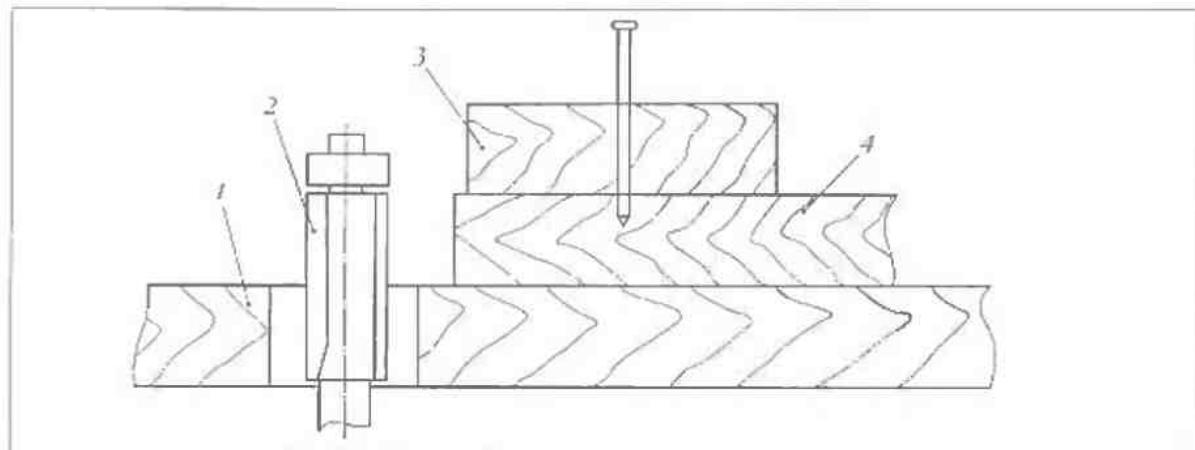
Фрезерование кромок деталей по контуру с помощью шаблона: 1 – рабочий стол; 2 – проходная фреза с подшипником; 3 – шаблон (линейка); 4 – обрабатываемая деталь.
